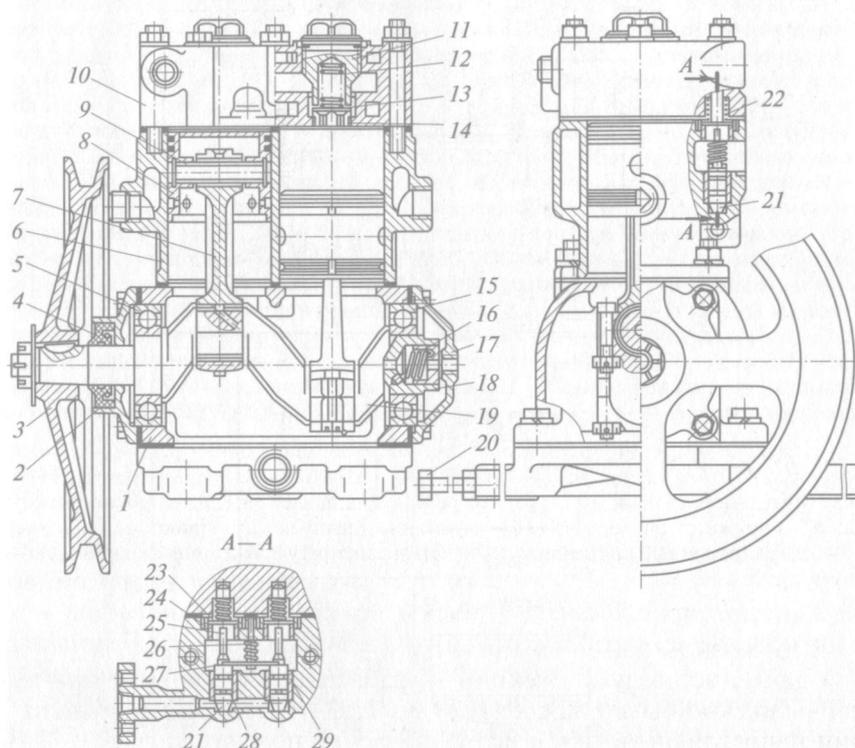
Компрессор пневматического привода тормозов автомобиля ЗИЛ-130:
